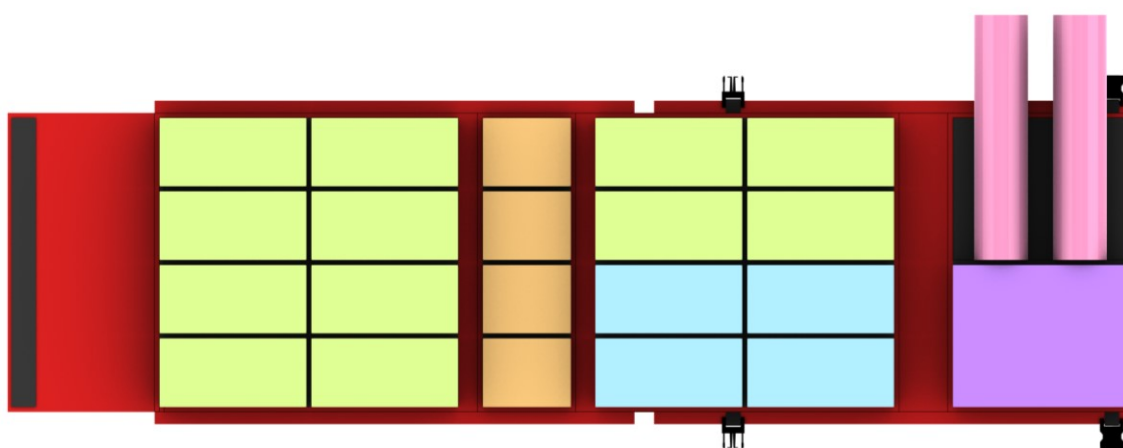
Horizontálně orientovaný organizér varianta 1
